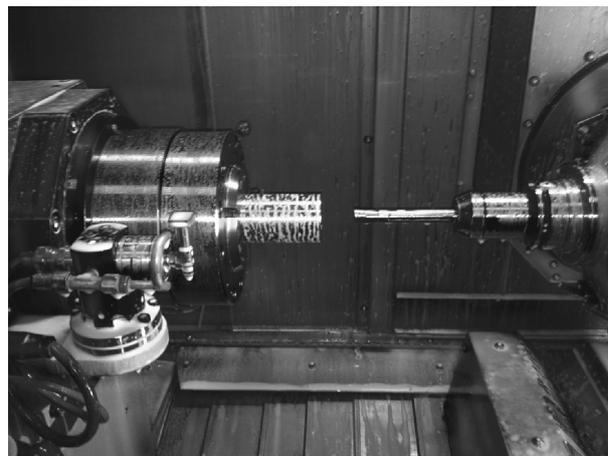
Растачивание образца на фрезерно-токарном станке с ЧПУ Willemin Macodel
